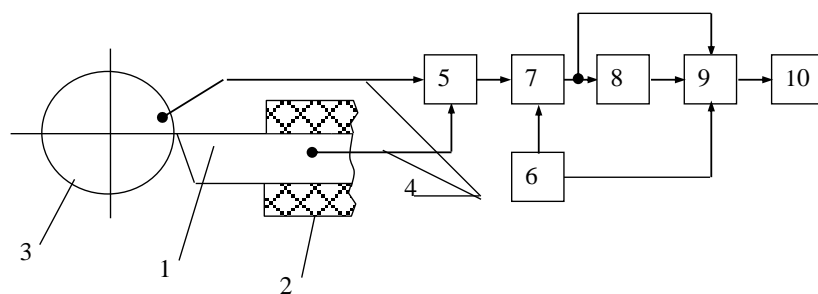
Спосіб визначення зносу різального інструмента для металооброблювальних верстатів з ЧПК
